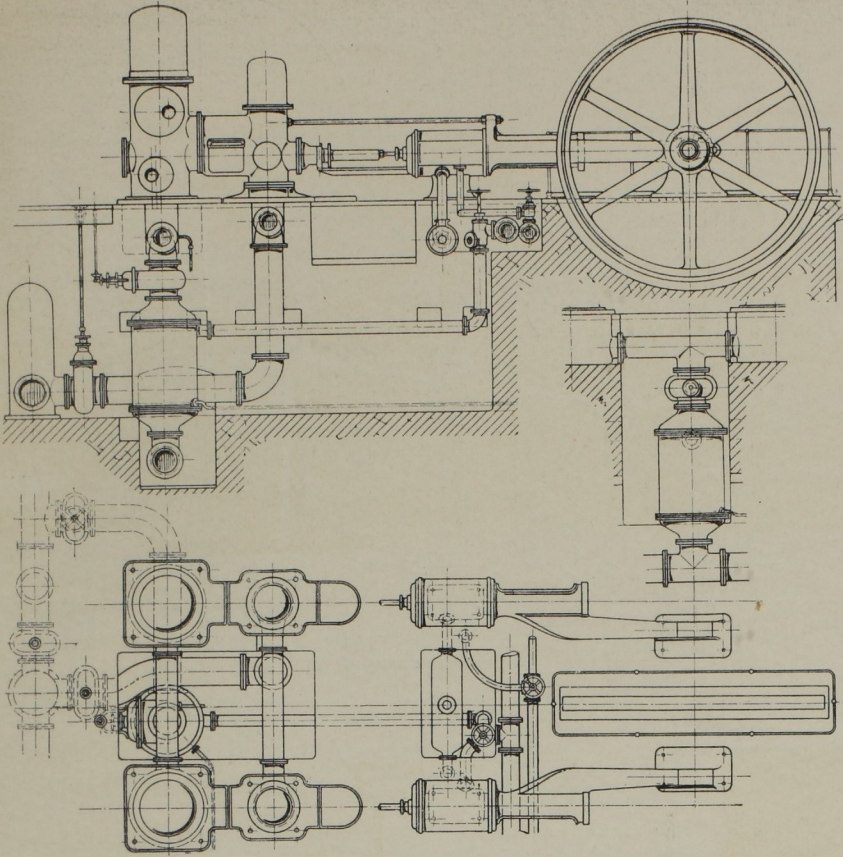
Seitenansicht und Grundriss der Pumpmaschinen.
